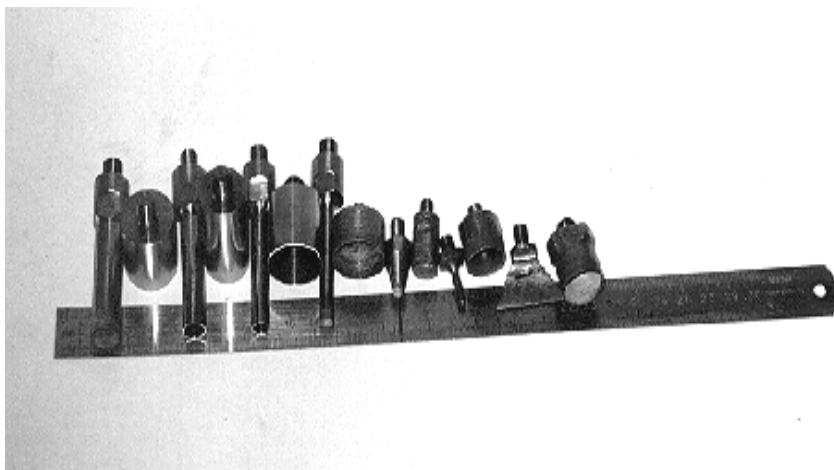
Рабочие инструменты для комплектации малогабаритных ультразвуковых колебательных систем
